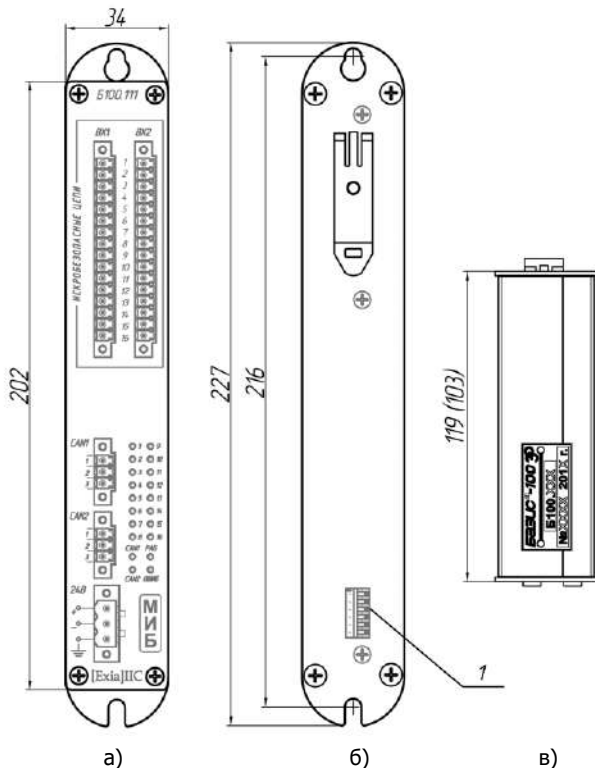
Вид корпуса Ш1 модуля Контроллера: а) спереди; б) сзади; в) сверху
